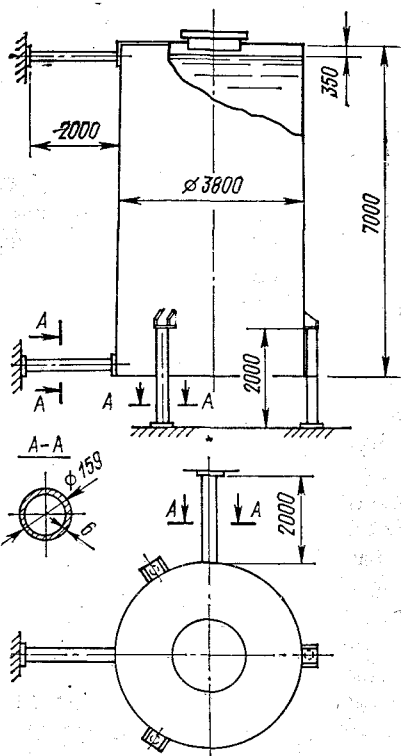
Цилиндрический резервуар на податливых опорах
